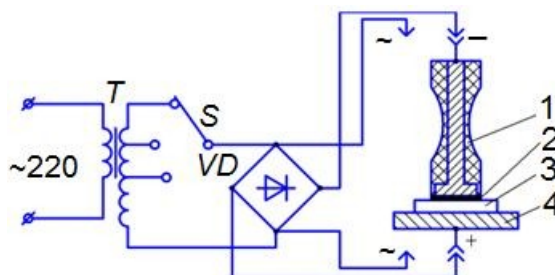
Схема установки для електрохімічного маркування: 1 – електрод-інструмент; 2 – трафарет; 3 – виріб; 4 – робочий стіл
